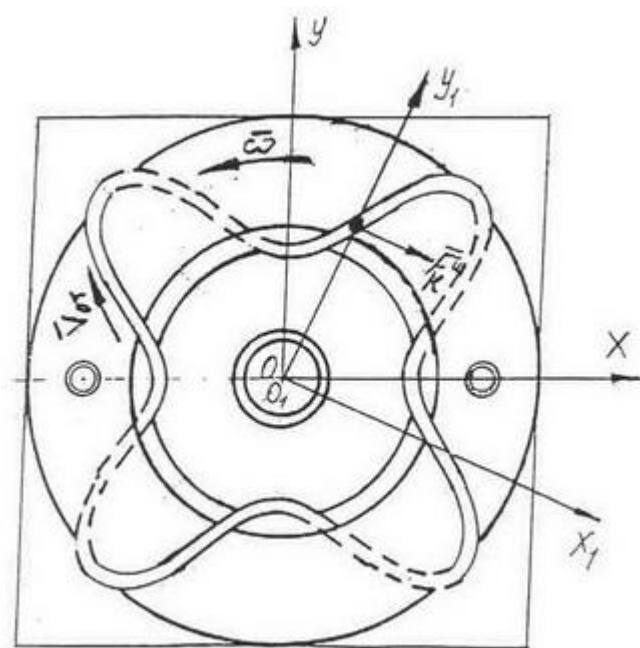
Торoidalный летательный аппарат-инерцид конструкции В.И. Докучаева (1996г). Сборочный чертёж, вид сверху
